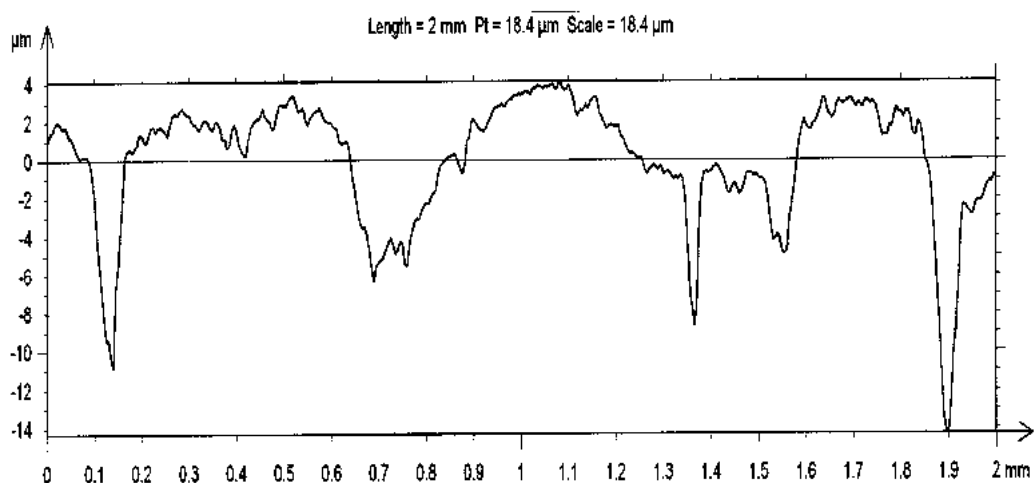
Переріз відфільтрованого профілю поверхні металевих деталей після фрезерування та обробки в торовій машині
